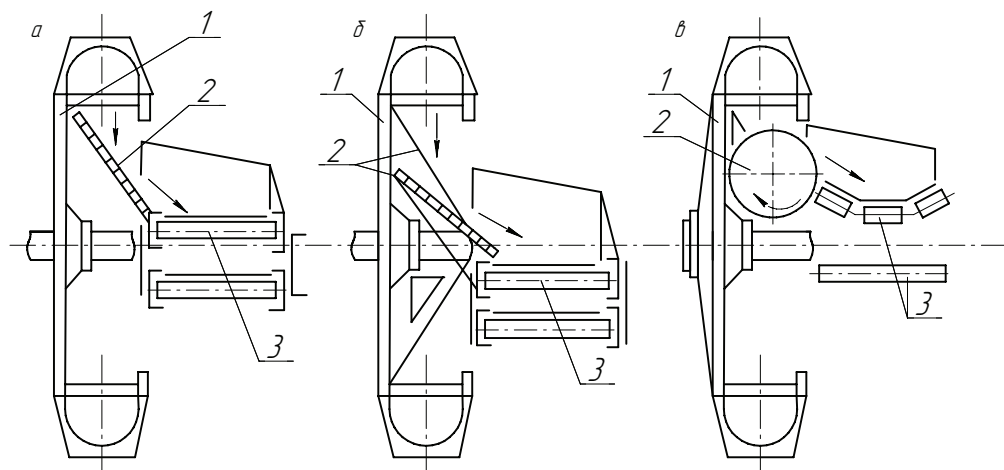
Конструктивные схемы приемно-питающих устройств ротора бескамерного типа:
